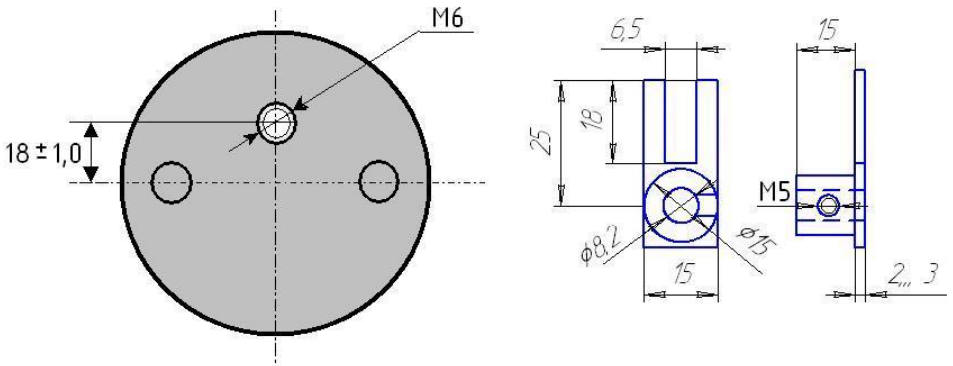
Доработка диска подшипника ходового колеса и редукторов лебёдок и пример изготовления поводка для датчиков вылета высоты и пути
